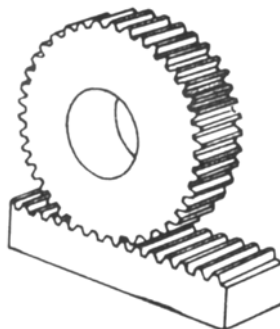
Engrenagem cilíndrica de dentes retos com cremalheira^[13]
